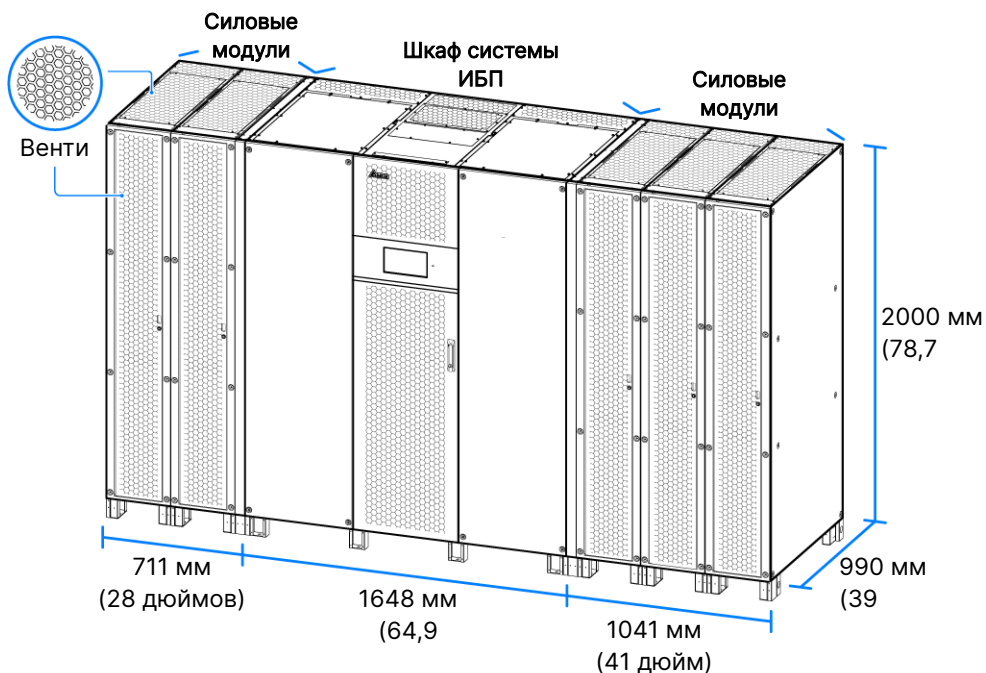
ИБП 1250 кВА_ Внешний вид и размеры
